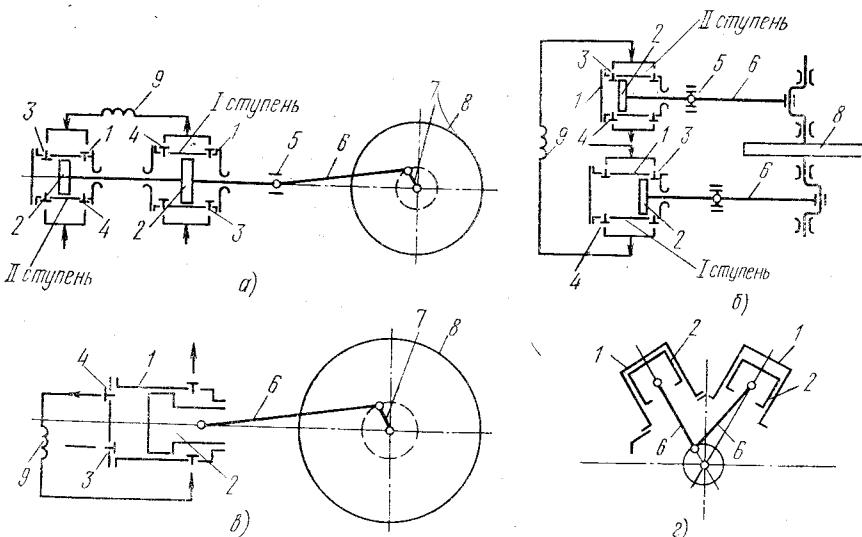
Схемы многоступенчатых поршневых газовых компрессоров:
